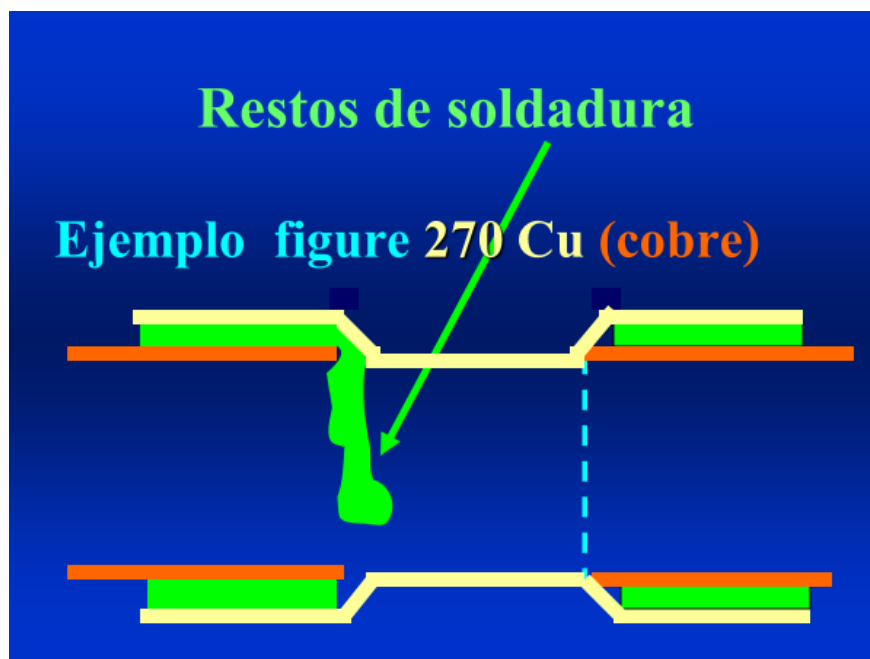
Ejemplo de entrada de soldadura por no estar el tubo haciendo tope en el accesorio en la zona izquierda (Fig. 270Cu en amarillo)
